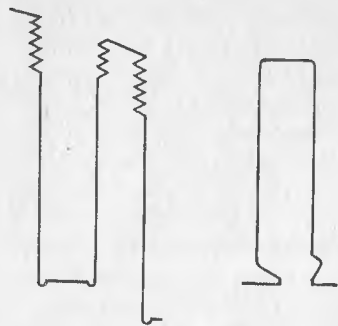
Паз обмотки ротора, наматываемой на станке.
